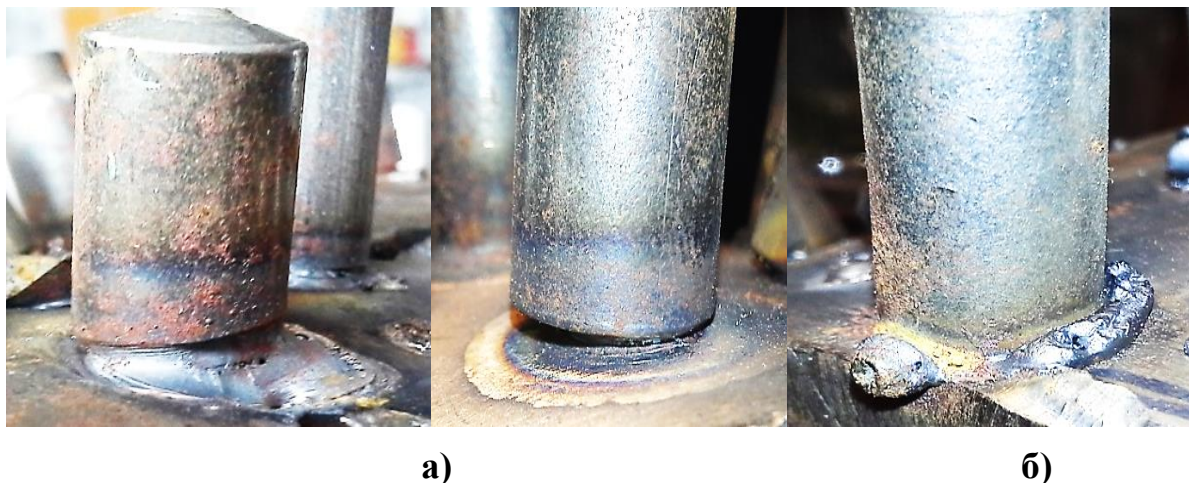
Фрагменти зварних з'єднань шип (сталь20) – труба (сталь 15X5M)
